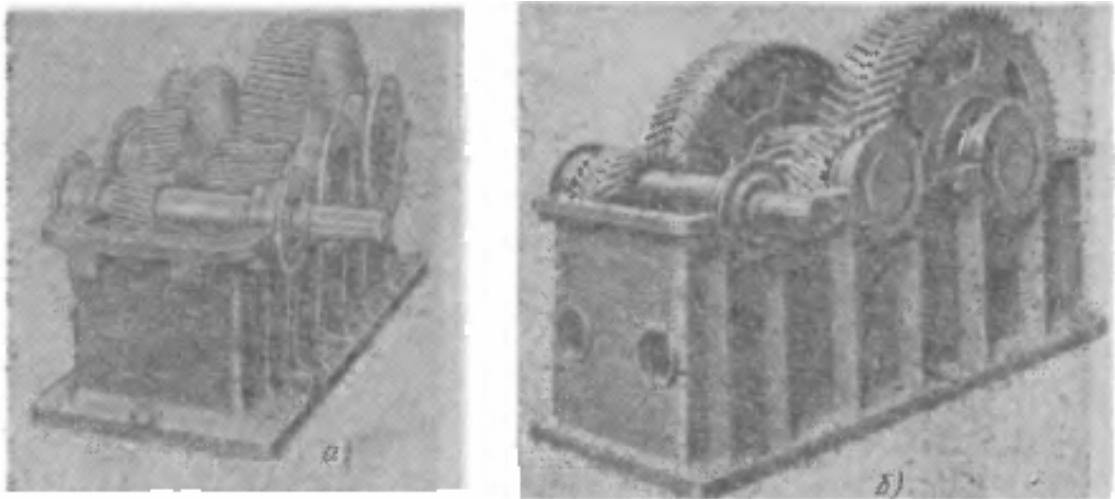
Конструктивные разновидности цилиндрических двухступенчатых горизонтальных редукторов с развернутой схемой
